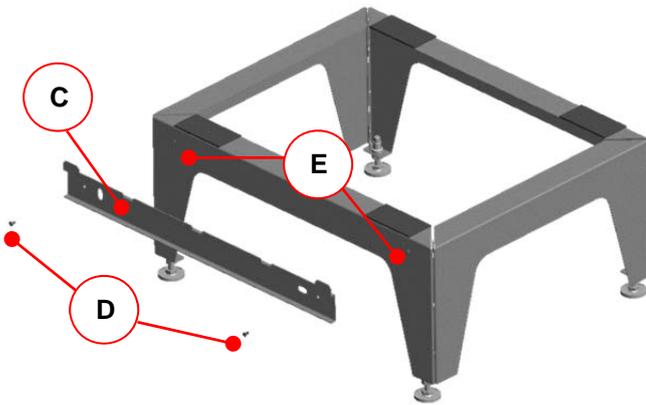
Montage des Befestigungsbleches an das Fußteil
